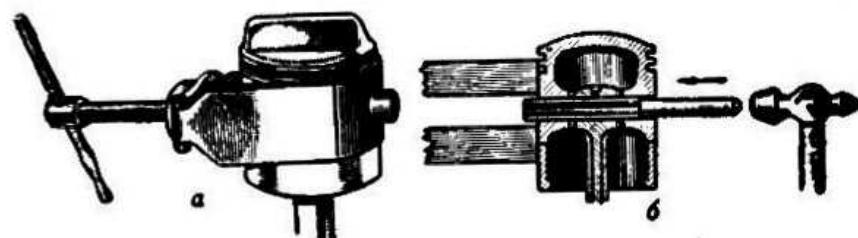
Различные способы выпрессовки пальца из бобышек поршня
